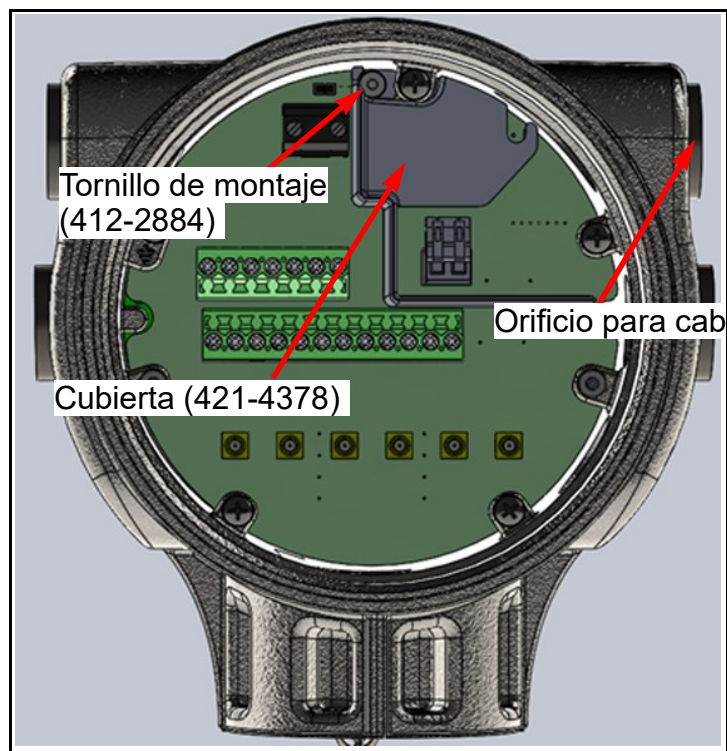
Cubierta FISCO y tornillo de montaje instalados
